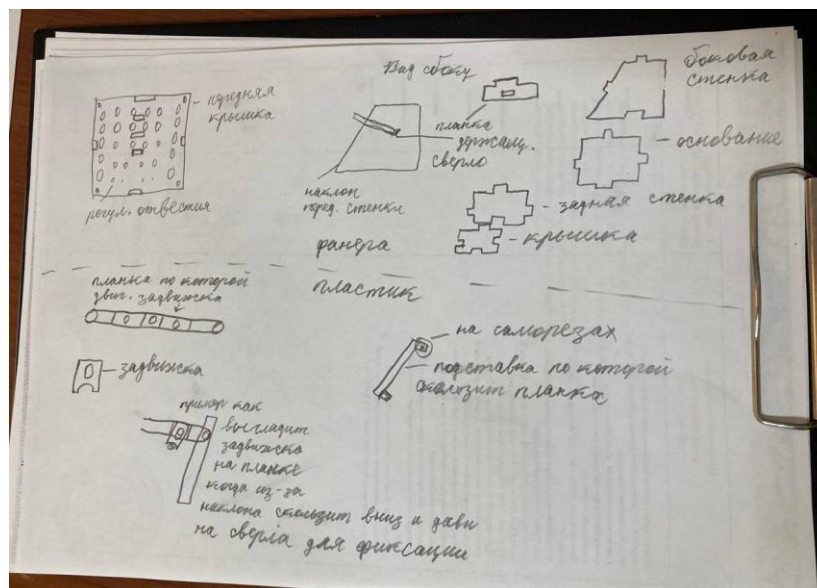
Наброски вида органайзера и его сборочных деталей
